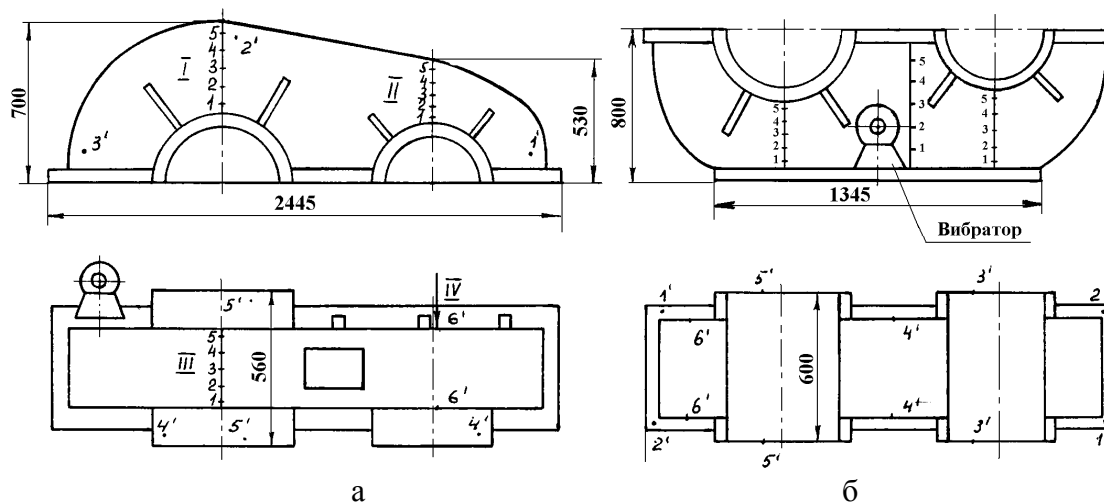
Схема расположения базовых точек для замера деформаций на крышке (а) и корпусе редуктора (б)
